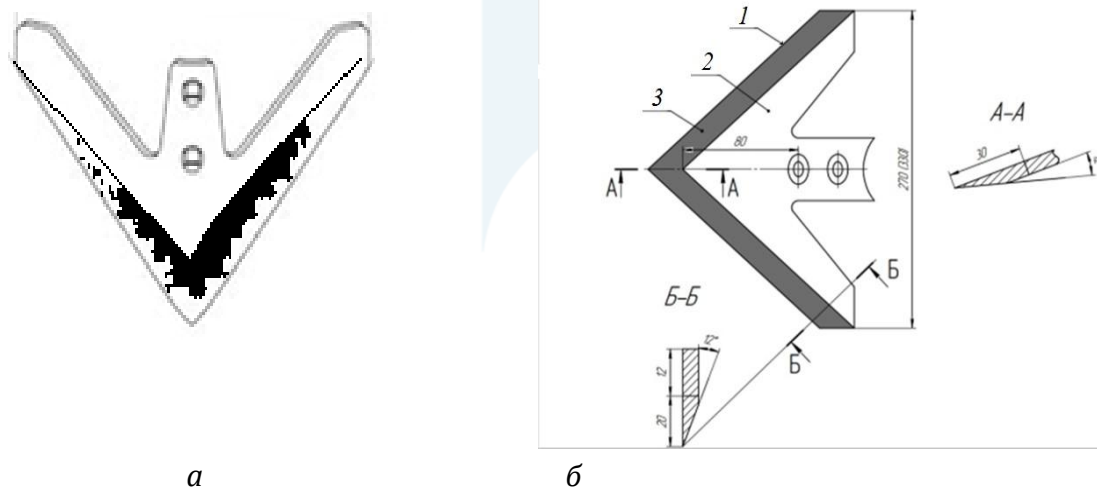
Изменение профиля при изнашивании: а — лапы культиватора с изношенной поверхностью, б- Схема восстановления стрелчатой лапы культиватора. 1-зона наплавки, 2-восстанавливаемая деталь, 3-угловая пластина.
